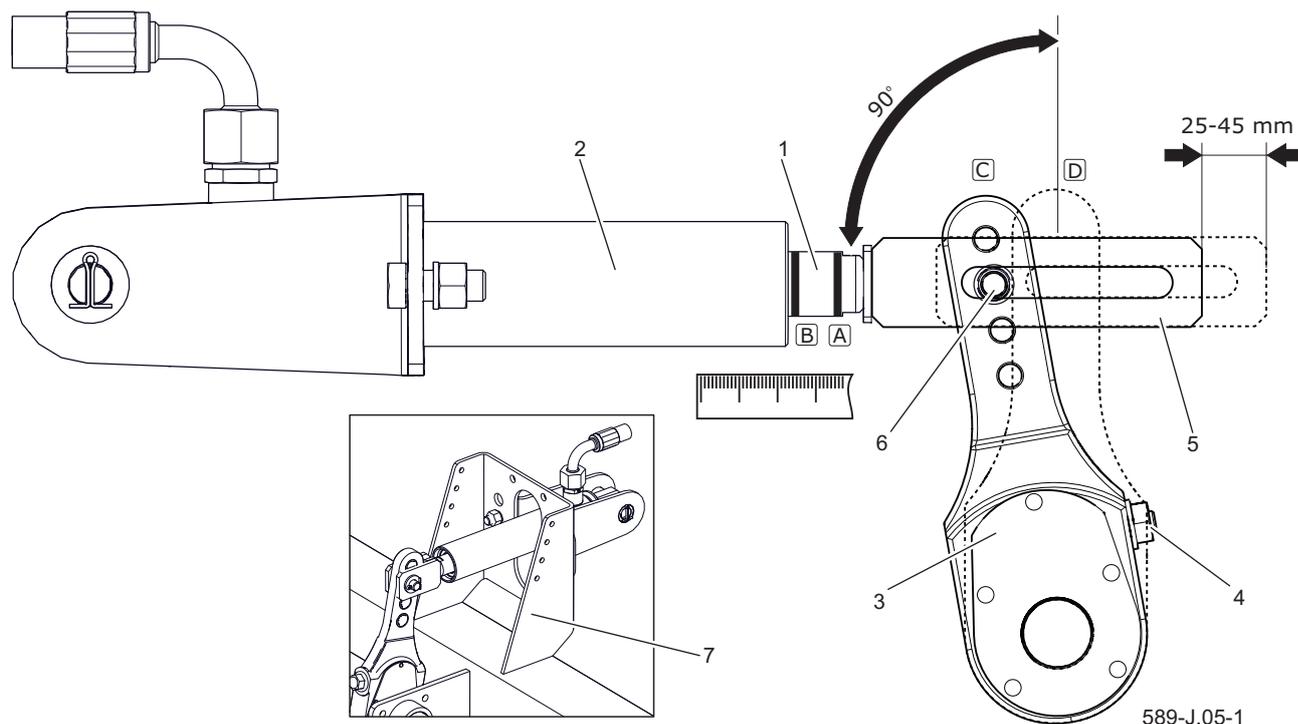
Принцип регулировки пневматического тормоза
